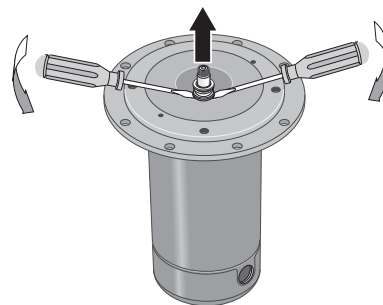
RETIRER LA PLAQUE D'ÉTANCHÉITÉ
